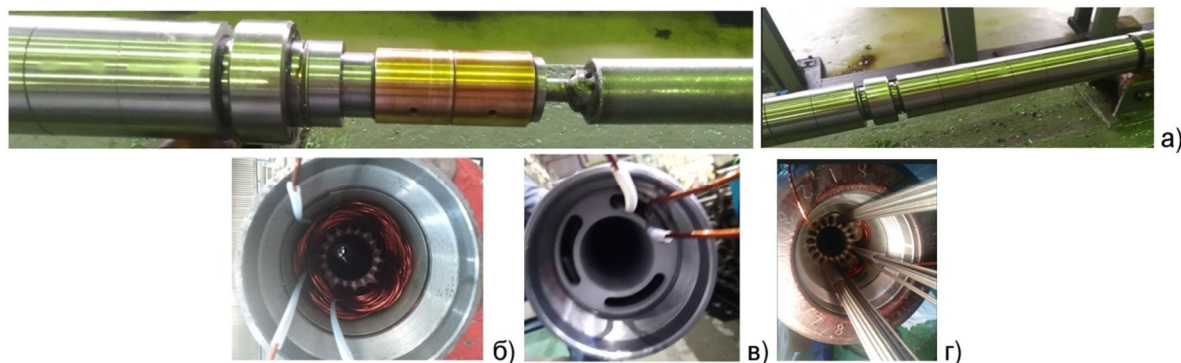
Вентильный погружной односекционный электродвигатель производства ООО «Ремера-Алнас»: а) общий вид; б) статор с запрессованным магнитопроводом; в), г) пазы статора с пазовой гильзой из фторопластовой трубки и протяжной трехфазной обмоткой
